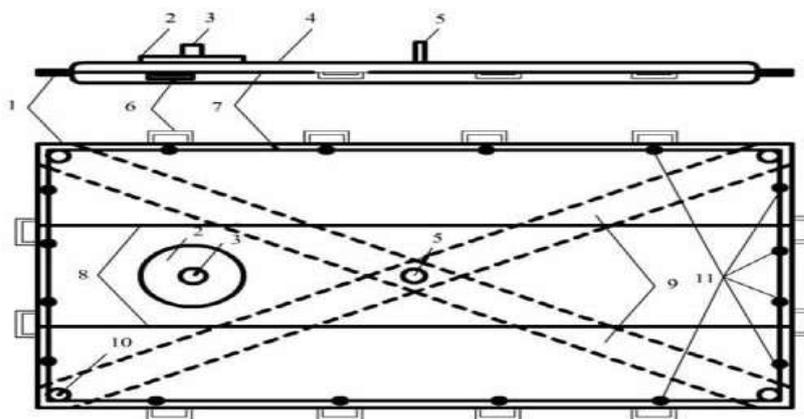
Принципиальная схема устройства полимерных эластичных резервуаров: 1 — торцевой шов; 2 — люк-лаз; 3 — сливно-наливной патрубков; 4 — верхнее полотнище; 5 — воздушный патрубок; 6 — ручка; 7 — боковые швы; 8 — продольные швы; 9 — усилительные ремни (для ЭР-4); 10 — металлические грузовые скобы (для ЭР-4); 11 — металлические кольца крепления эластичных резервуаров на поверхностях с уклоном 0,01-0,03
